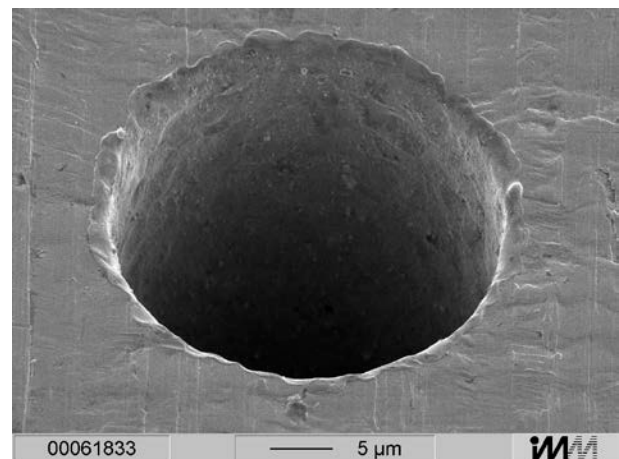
Eine Bohrung mit lediglich 20 µm Durchmesser erzeugt mit einer Senkerodiermaschine, die mit der Vibrationsbohrspindel ausgestattet war (Bild: ICT-IMM)
